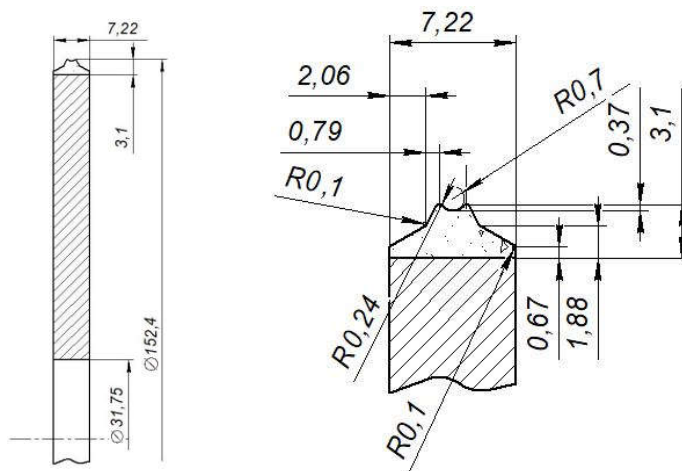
Профиль алмазного круга для обработки канавок концевой фрезы (ширина круга $B=7,22$ мм, глубина шлифования $t=2,45$ мм)
